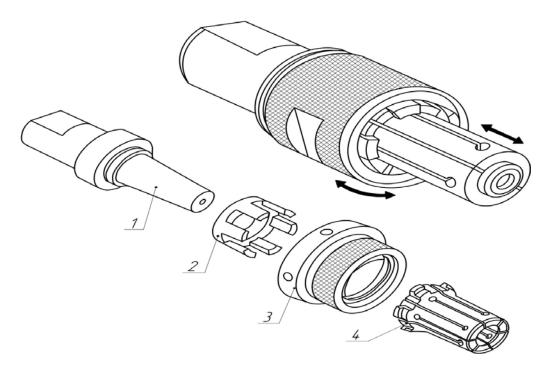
Оправка с разжимной цангой: 1 — оправка; 2 — втулка; 3 — гайка; 4 — цанга
